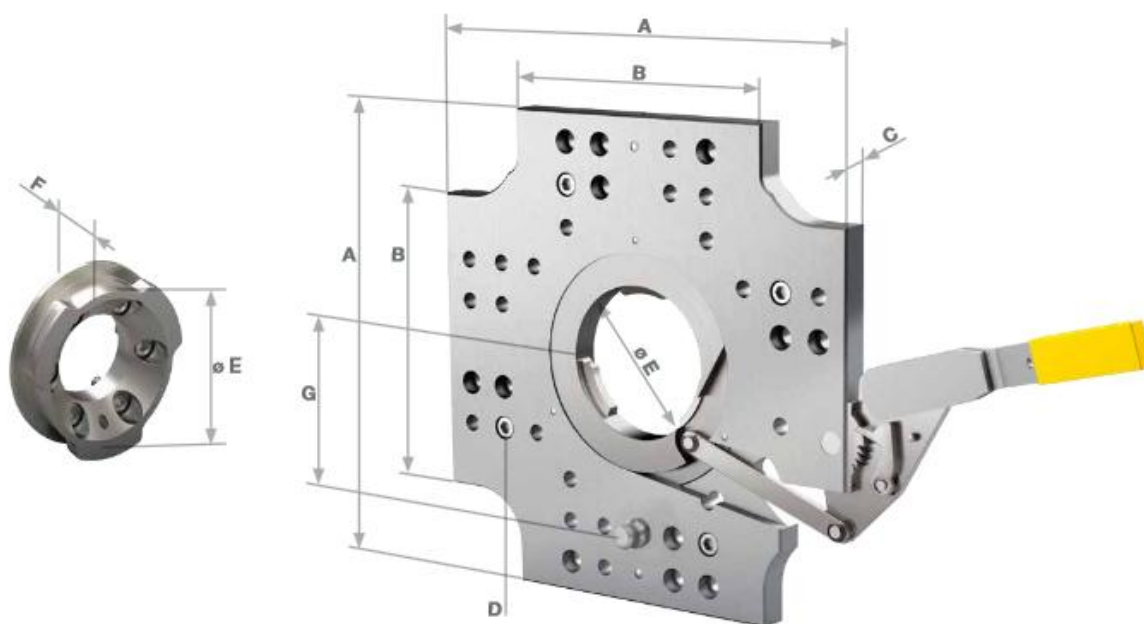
Hydraulické upínání firmy STÄUBLI(9)
